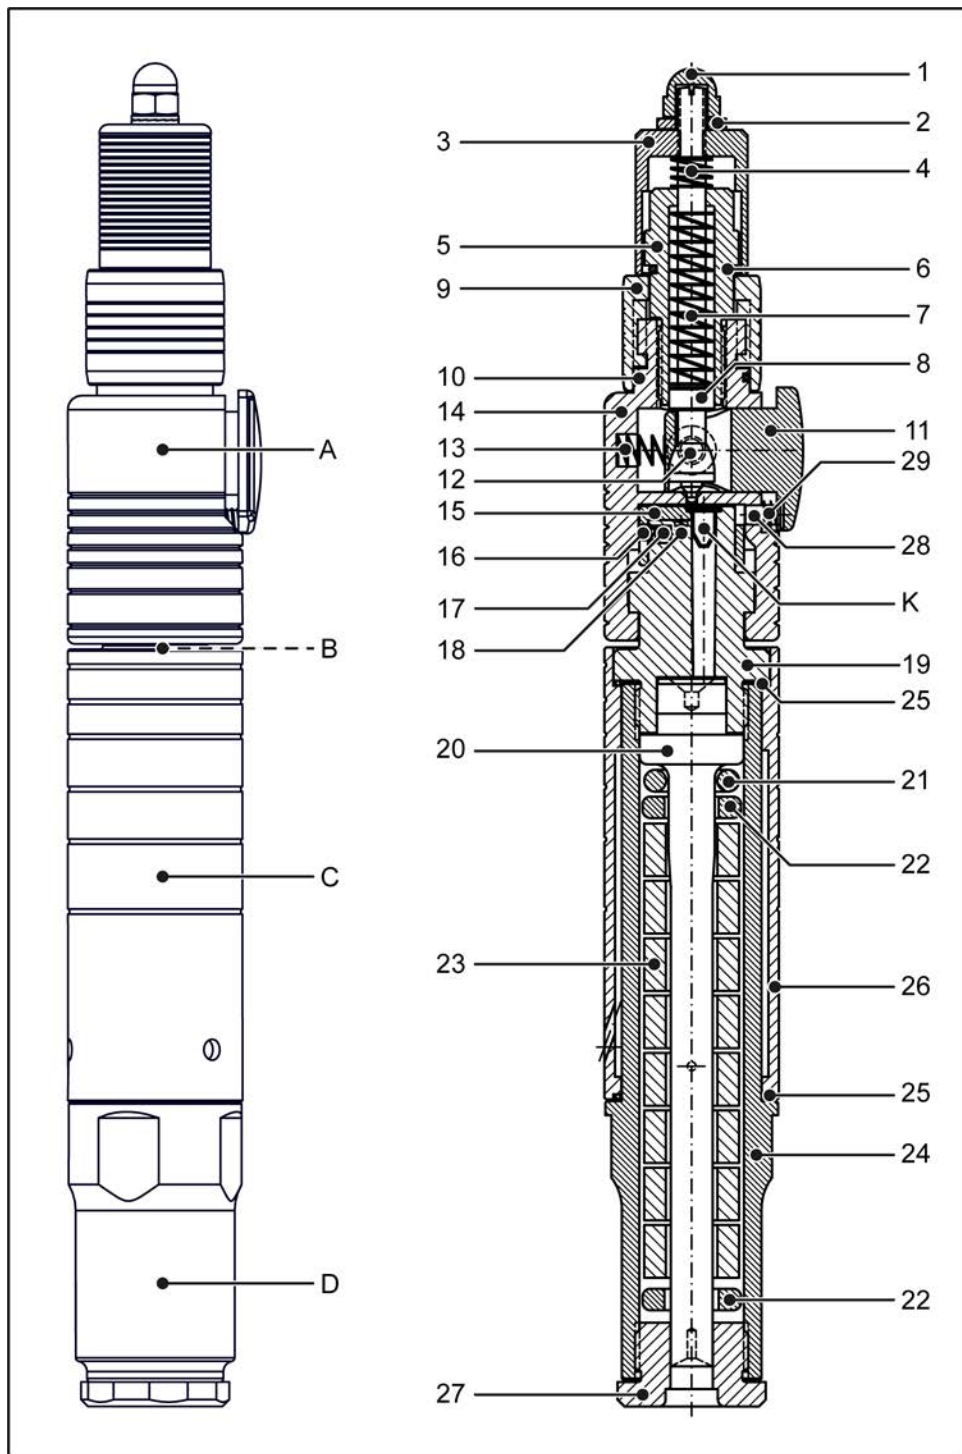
Baugruppen/Bauelemente Typ KS
